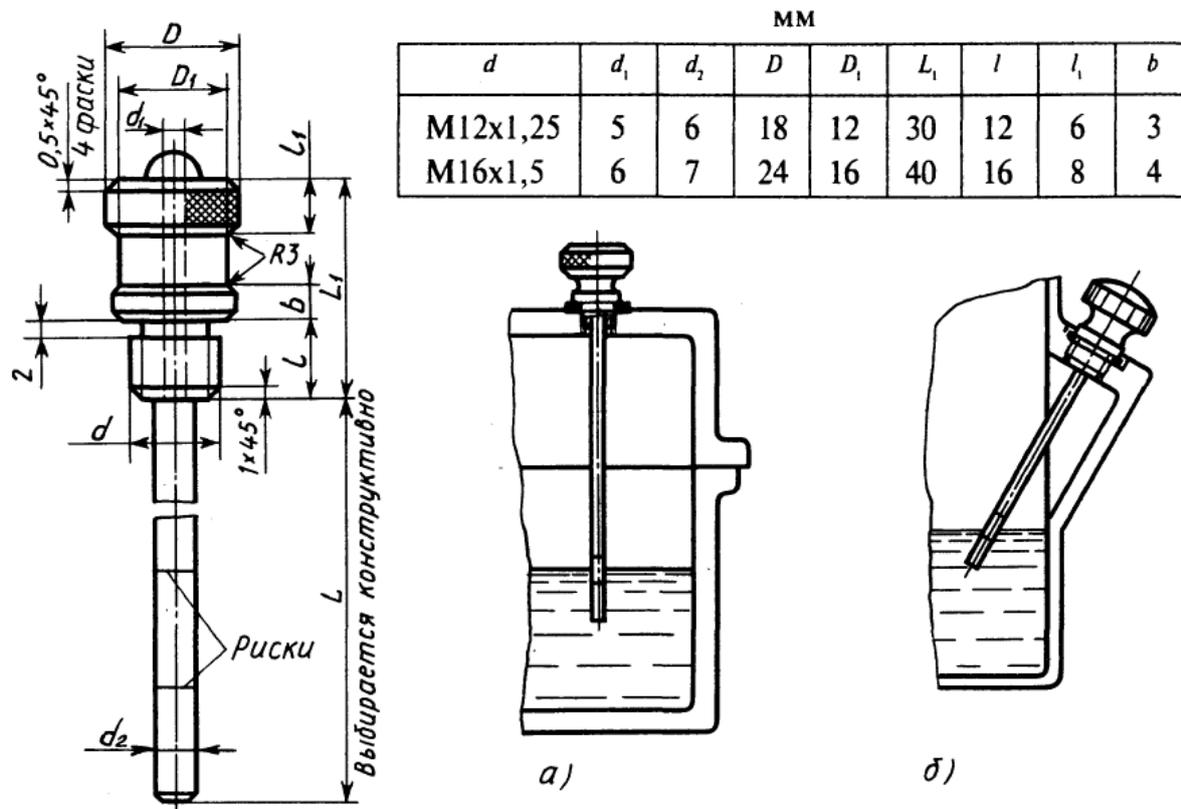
Жезловый маслоуказатель и способы его установки на корпусе:
